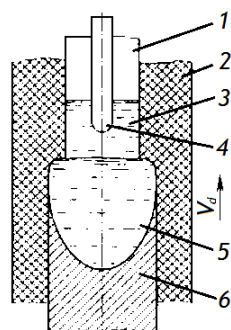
Электрошлаковая сварка, где 1 – изделие, 2 – формирующее приспособление, 3 – расплавленный шлак, 4 – металлический электрод, 5 – сварочная ванна, 6 – сварной шов
